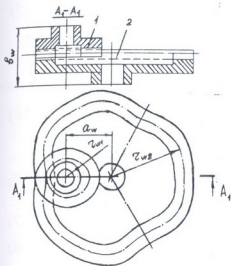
Торцевая зубчатая передача с некруглыми колесами
